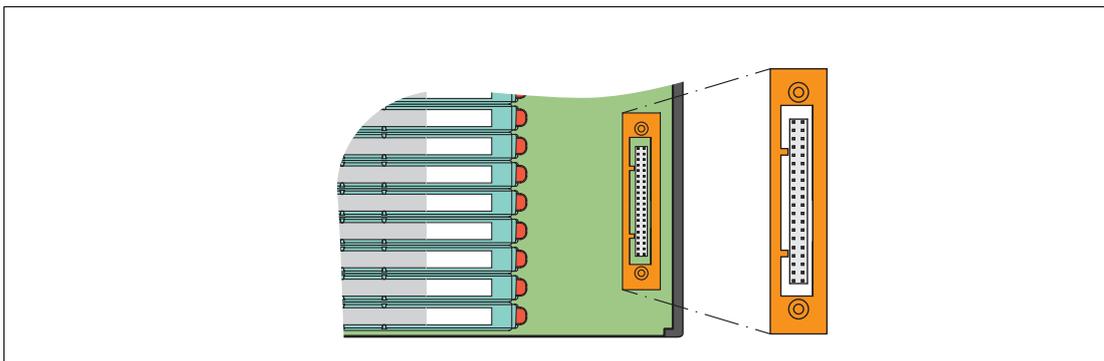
Anschlussbeispiel steuerungsseitiger Systemstecker
